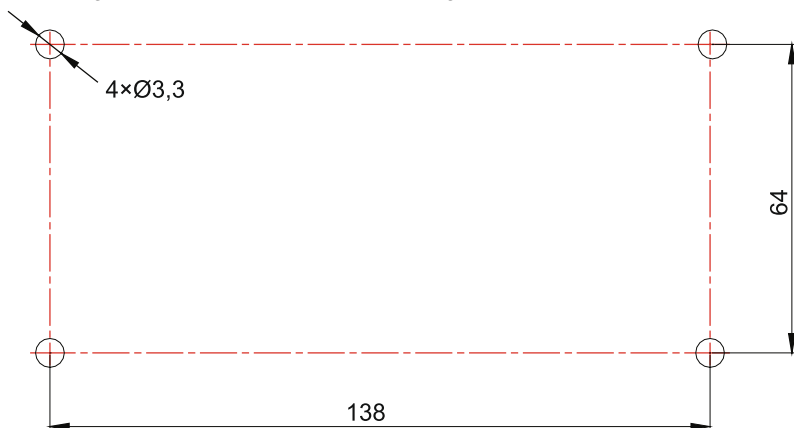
Fori per il montaggio della scatola di montaggio
